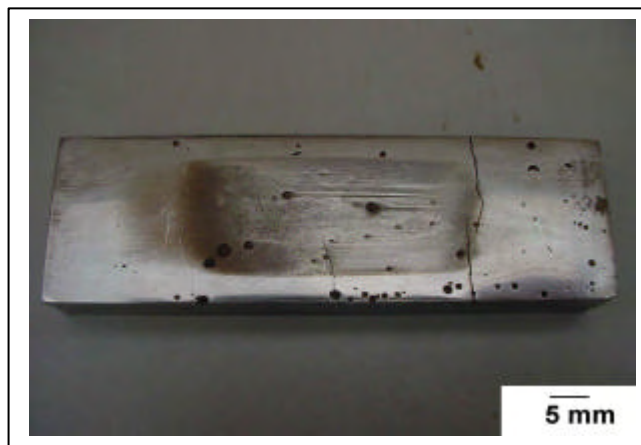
Corpo de prova 100D, soldado com 100 amperes com depósito de duas camadas.
